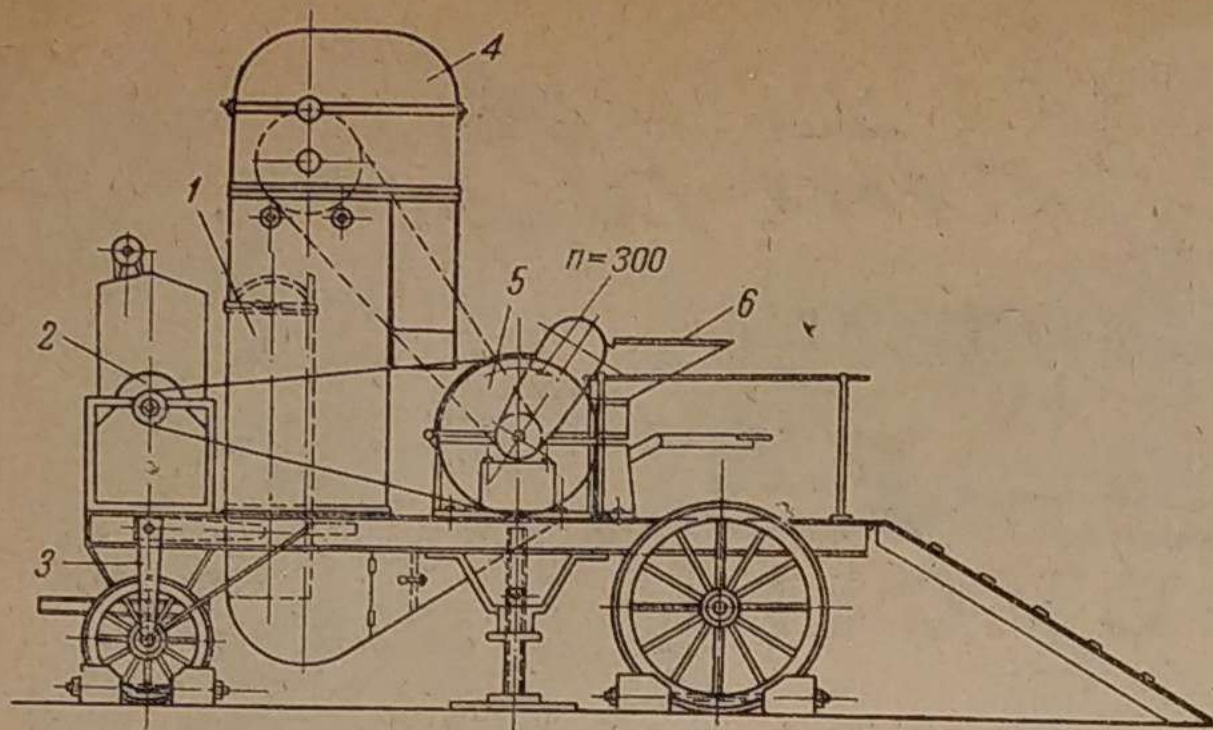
Машина для заготовки древесного газогенераторного топлива.
